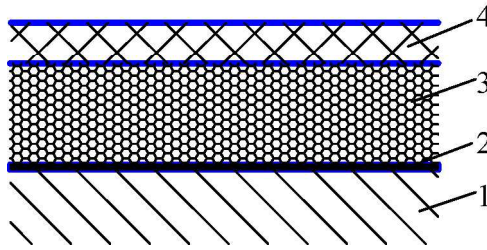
Структура материала эластичного металлофторопластового подшипника скольжения: 1 – корпус; 2 – клей; 3 – упругий слой из материала МР; 4 – фторопласт
